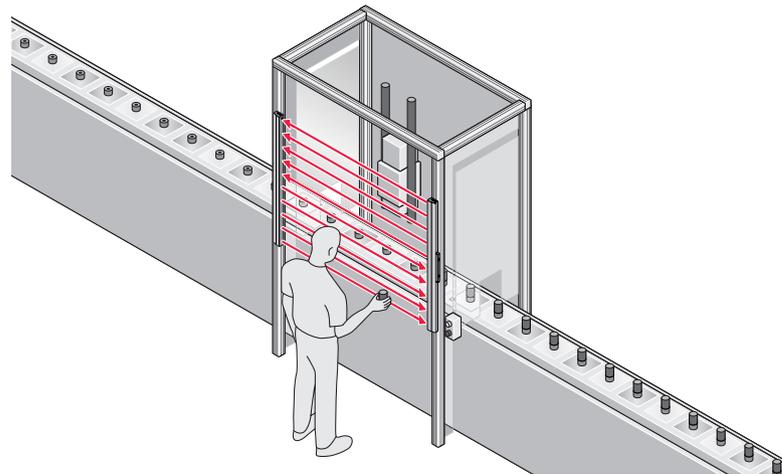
Exemple de montage avec la fixation C-Fix et la fixation L-Fix
